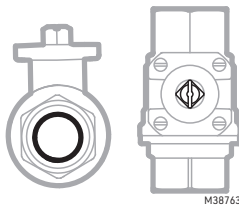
Beispiel für ein geöffnetes Kugelventil.
